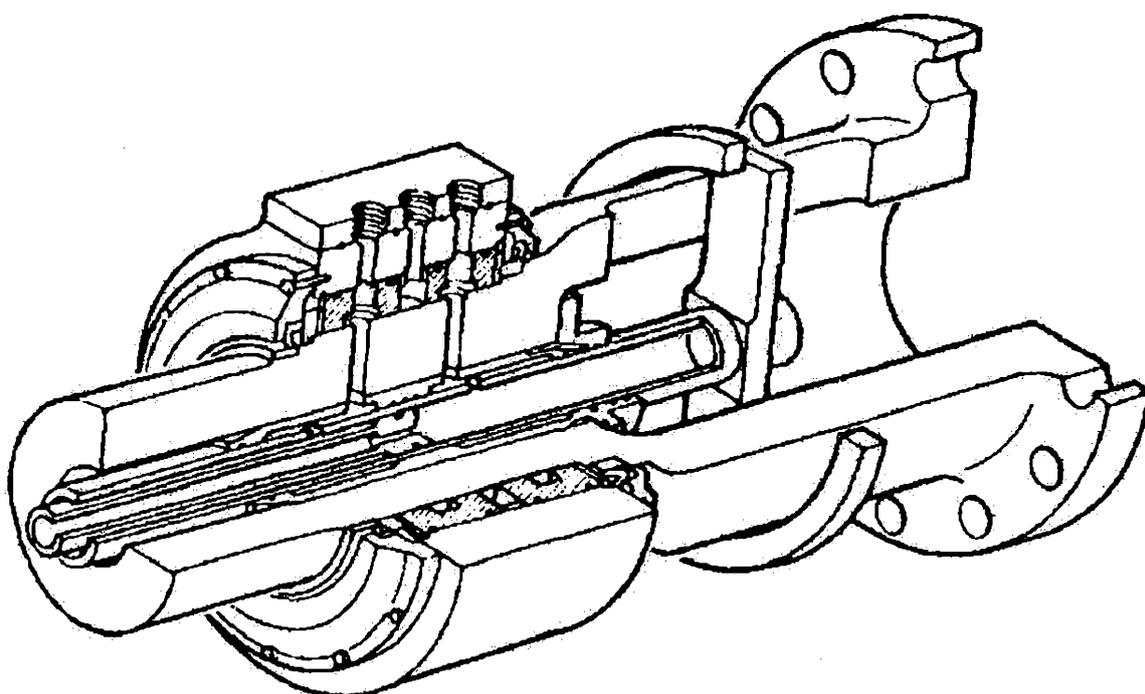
Узел распределительной коробки с уплотнительными кольцами высокого давления
